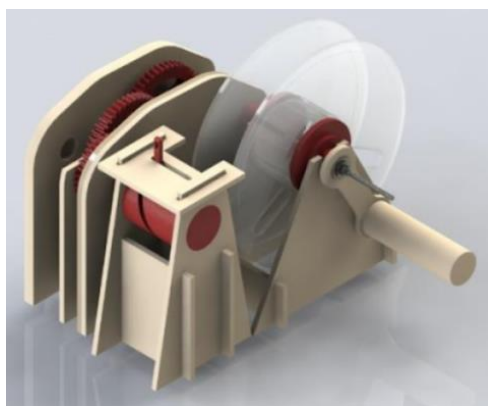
PREMIER PROTOTYPE DU BOBINAGE
